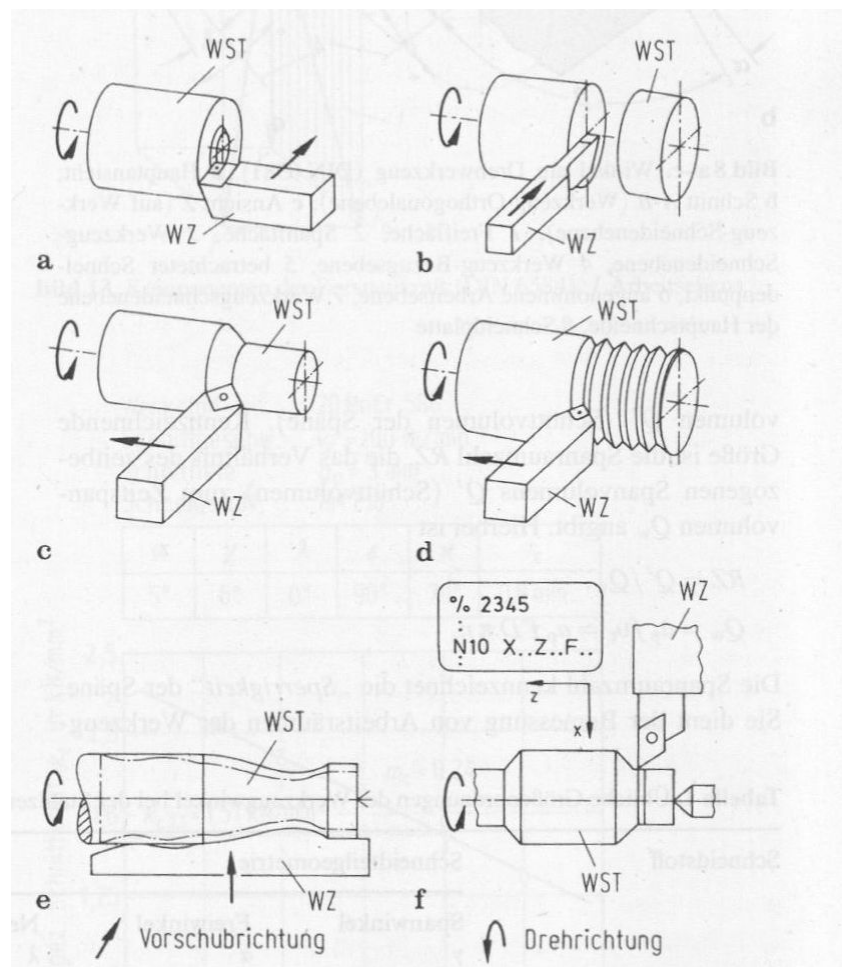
f. Drehfahren (DIN 8589 T 1). WST Werkstück, WZ Werkzeug.
